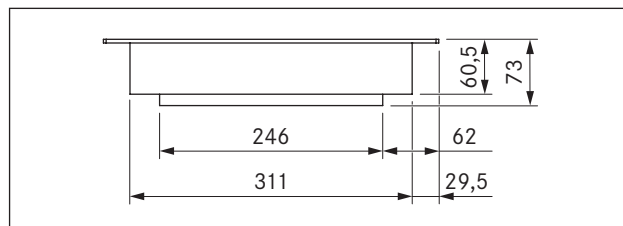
Dimenzije naprave gumba za upravljanje
